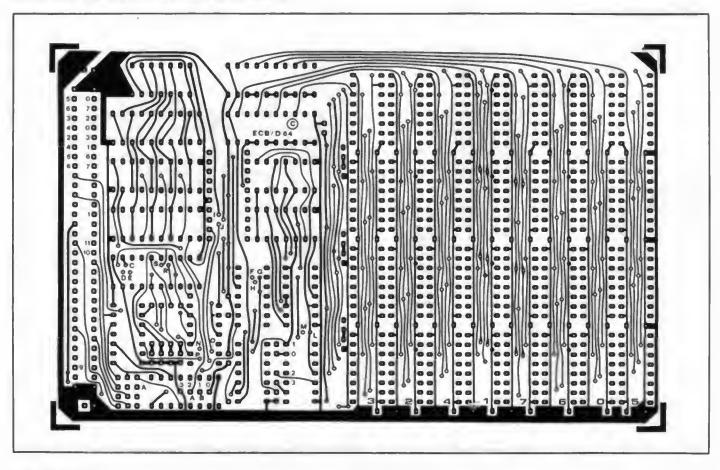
Das Platinenlayout. Oben die Bestückungsseite
